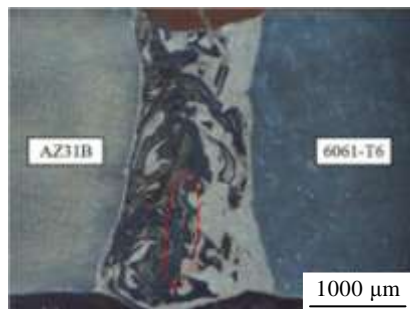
6061-T6/AZ31B 激光焊接接头截面形貌
